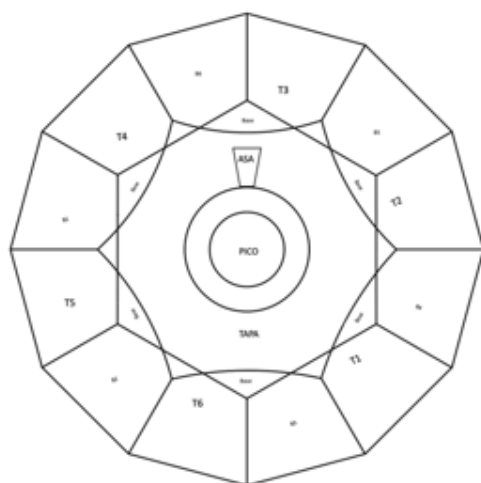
Plano superior del cuerpo de la botella, plano elaborado en AutoCAD.
